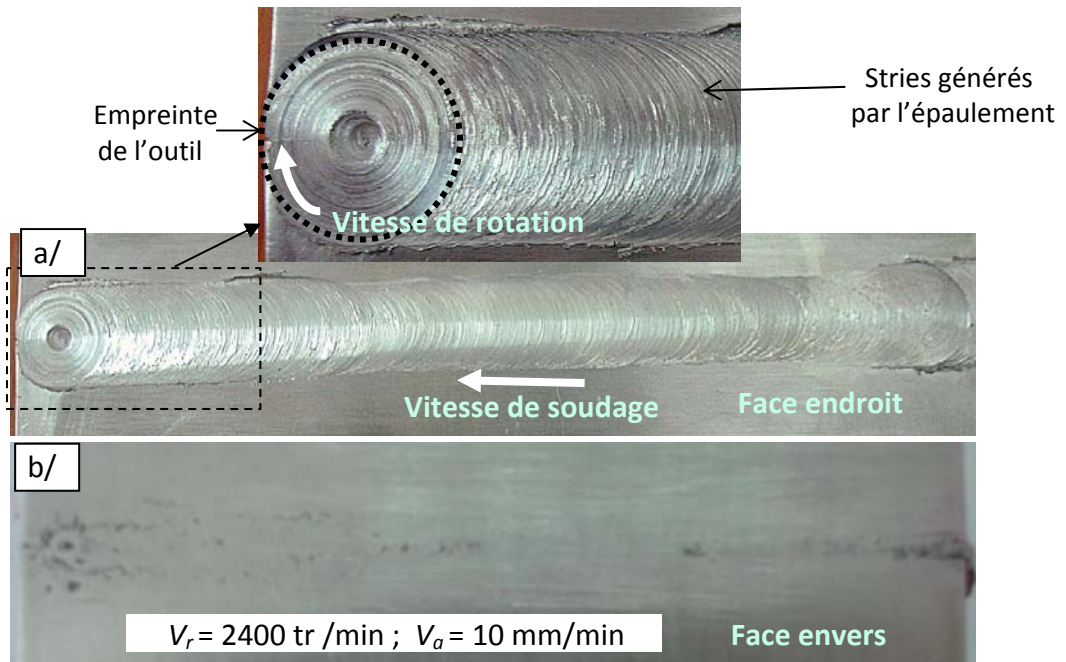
,b : Soudure sans défaut ; a/ Face endroit avec un agrandissement, b/ Face envers.
